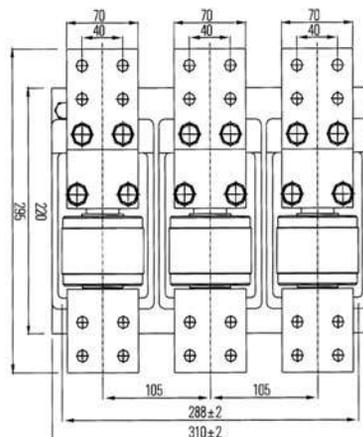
Габаритные размеры КВТ-1,14-1000/1250
